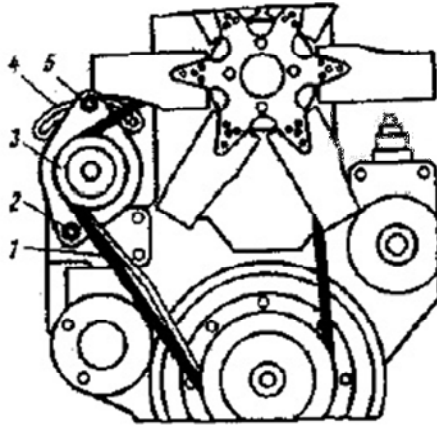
Устройство для натяжения ремня привода вентилятора и генератора двигателя СМД-14:
